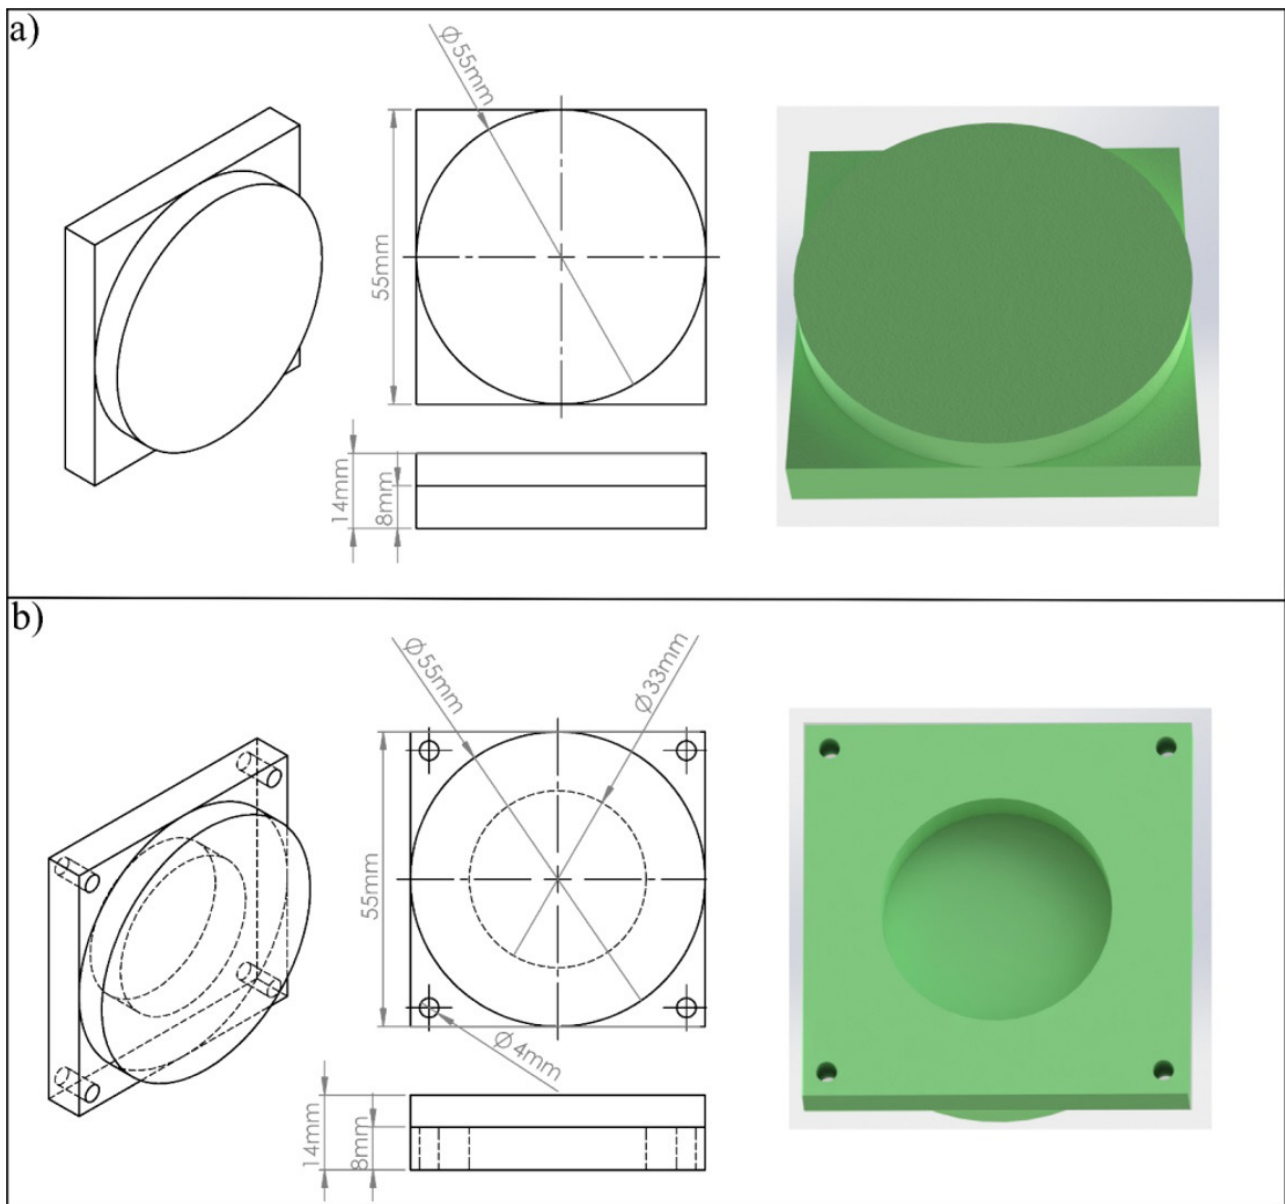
Modelo dimensionado para ser construído a partir da manufatura híbrida. (a) Adição de material por impressão 3D. (b) Remoção de material por fresagem CNC.
